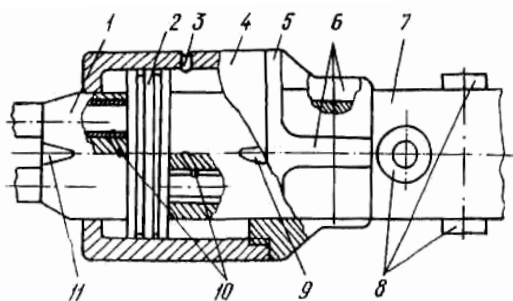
Одноциліндровий двокамерний двигун з рухомих циліндром
